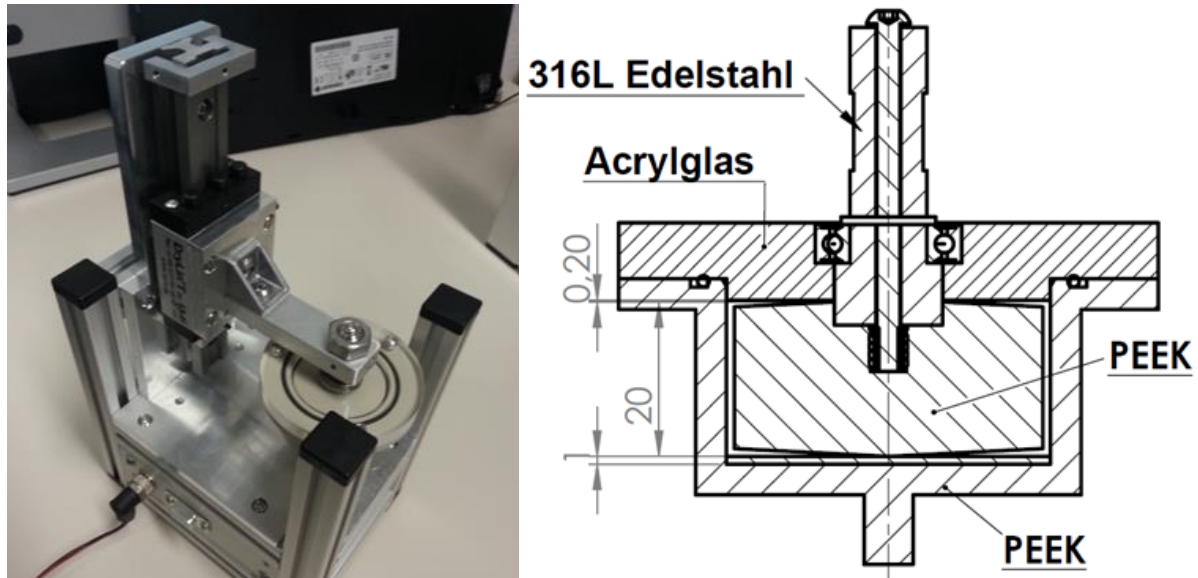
Prototyp des Scherapparats (links) und Schnitt der Couette-Baugruppe mit Materialien (rechts)
